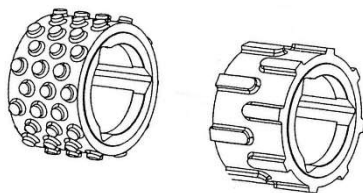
Схема знімної оболонки валка за заявками WO2006/133870A1 и DE102005027729A1
